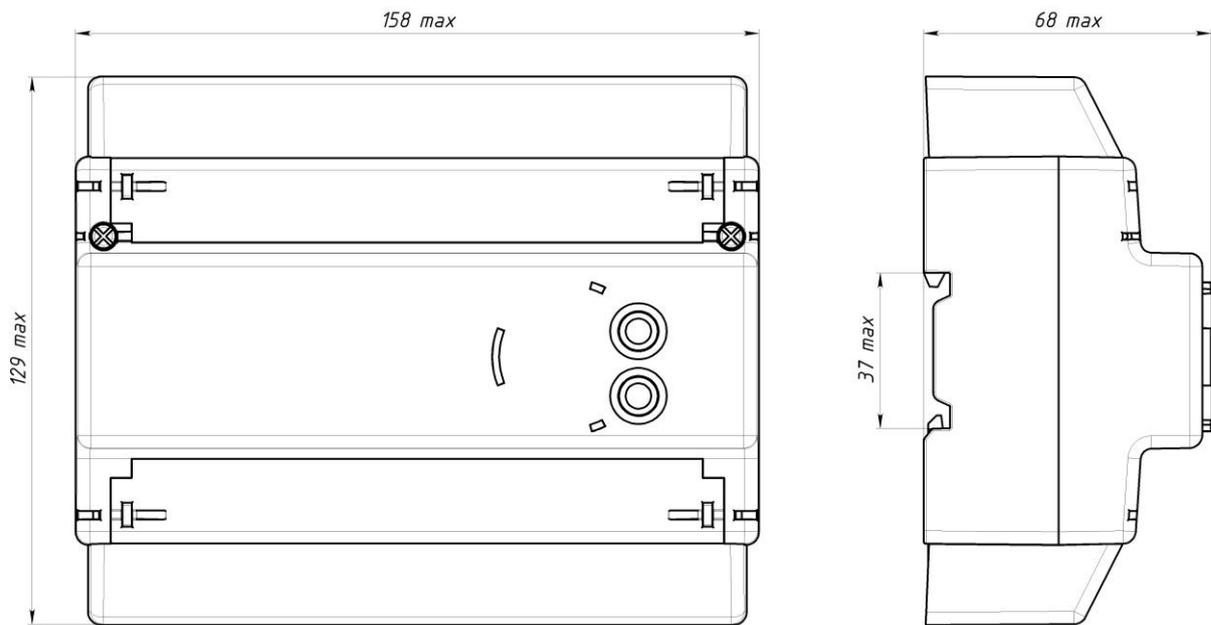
б – Корпус 9мТН35 со стандартными клеммными крышками
